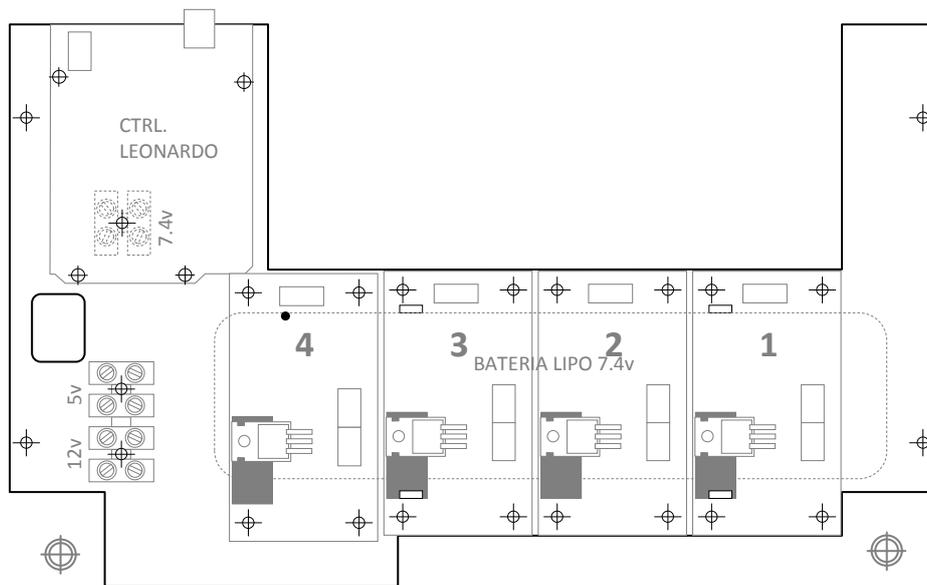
Vista en planta de la placa del primer nivel, y colocación de los dispositivos. Escala aprox. 1:2.
